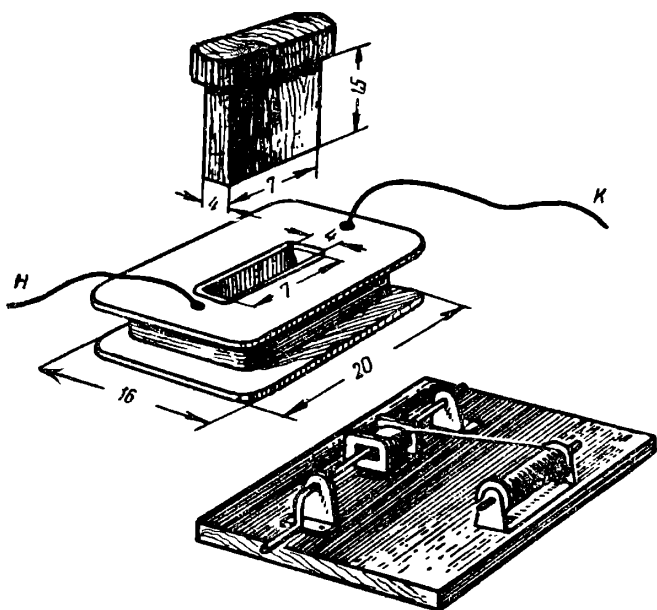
Каркас катушки и болванка. Приспособление для намотки
